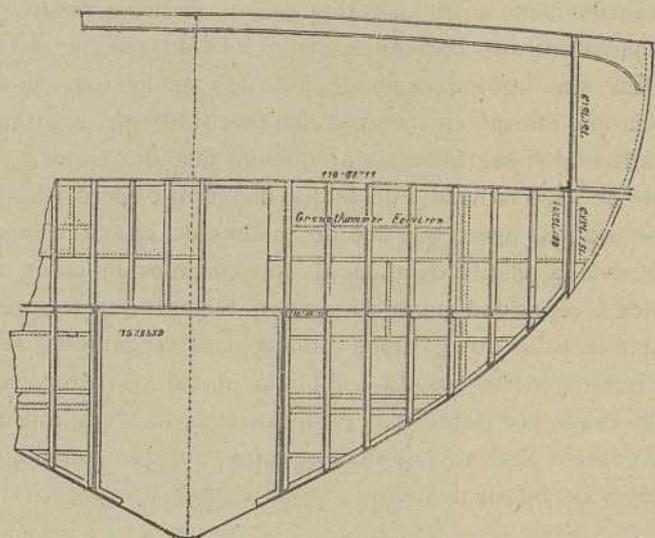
Tabique divisorio d. un buque de guerra moderno.
